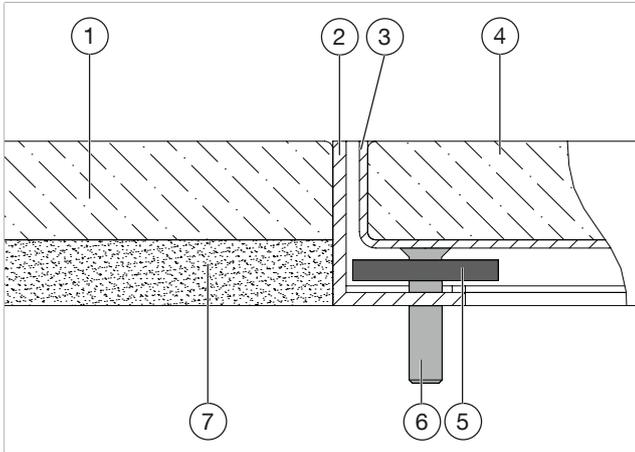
Befestigungsmagnet Wannentür ausrichten
